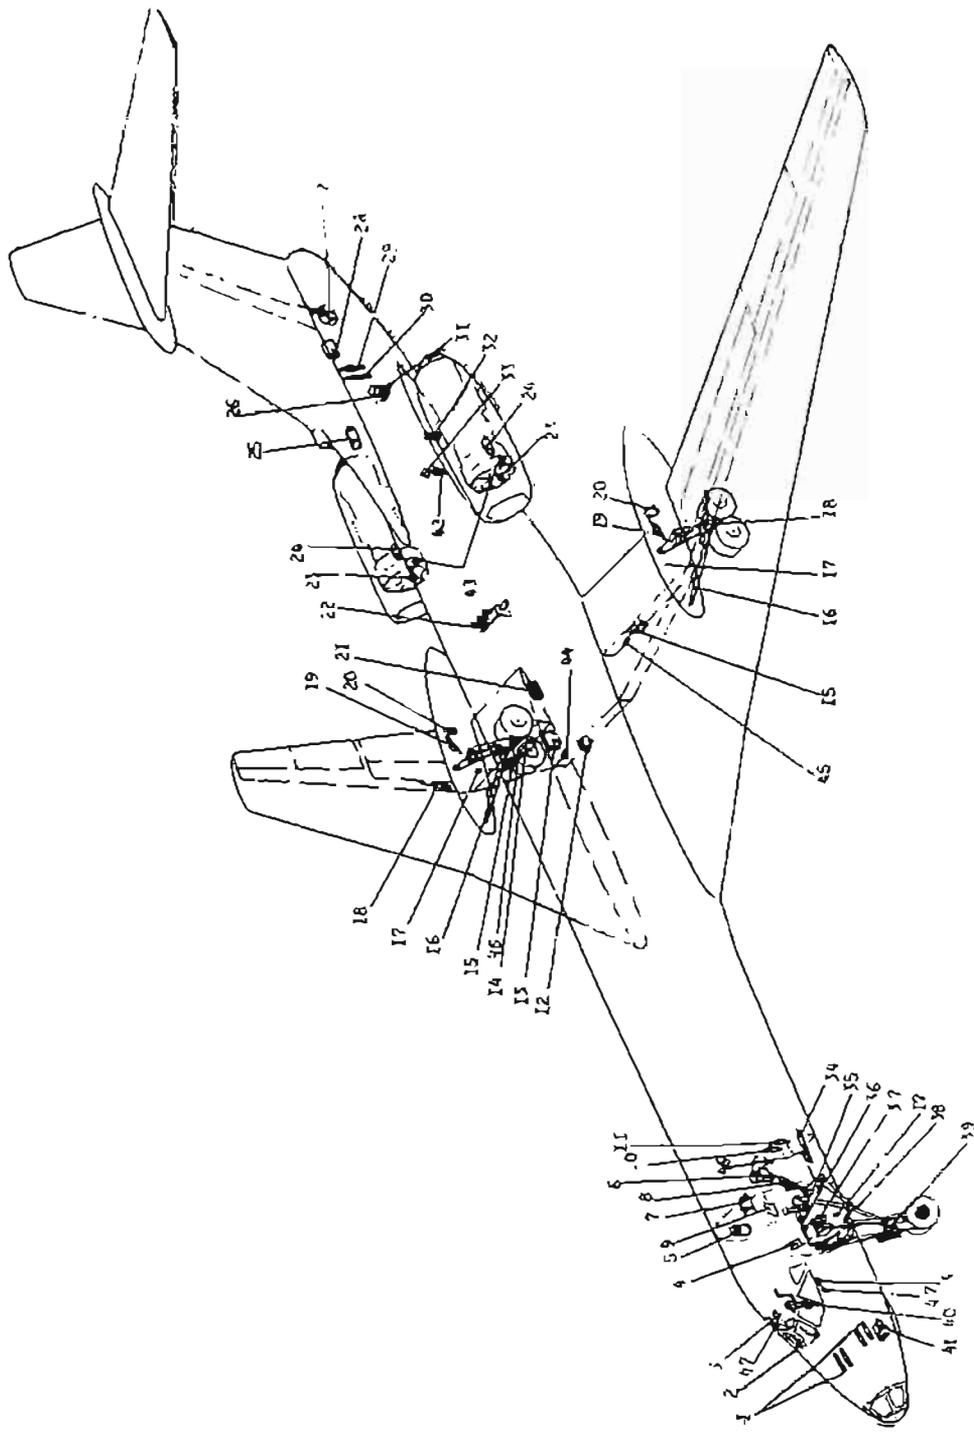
Anordnung der Geräte der Hydraulikanlage im Flugzeug
